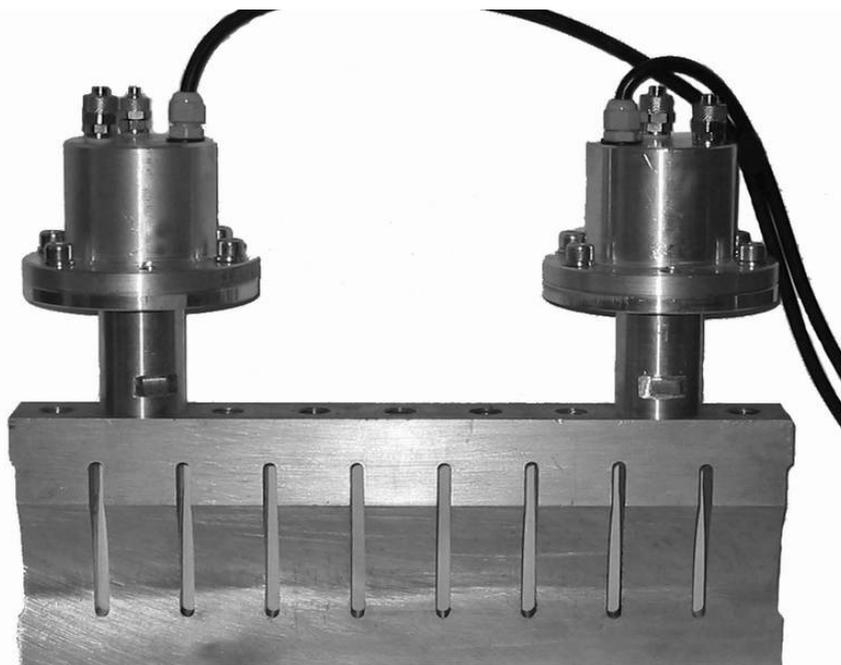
Ультразвуковая колебательная система для обеспечения сварного шва длиной 360 мм
